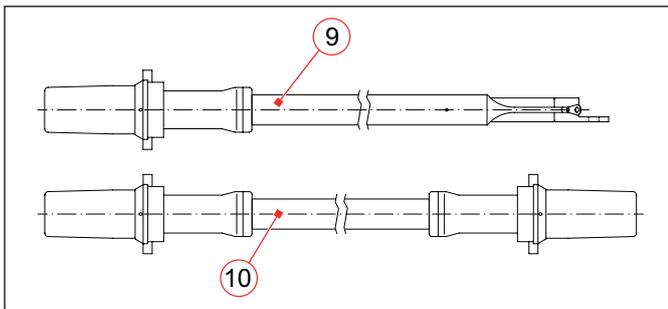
Ersatzteile für ZH 551/ZH 622 Stecker mit Anschlusskabel/Verbindungskabel
